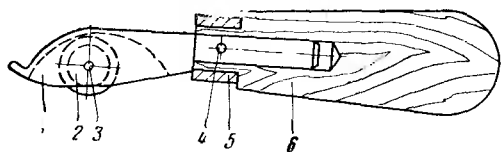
Приспособление для заправки замка уплотнителя стекла:
